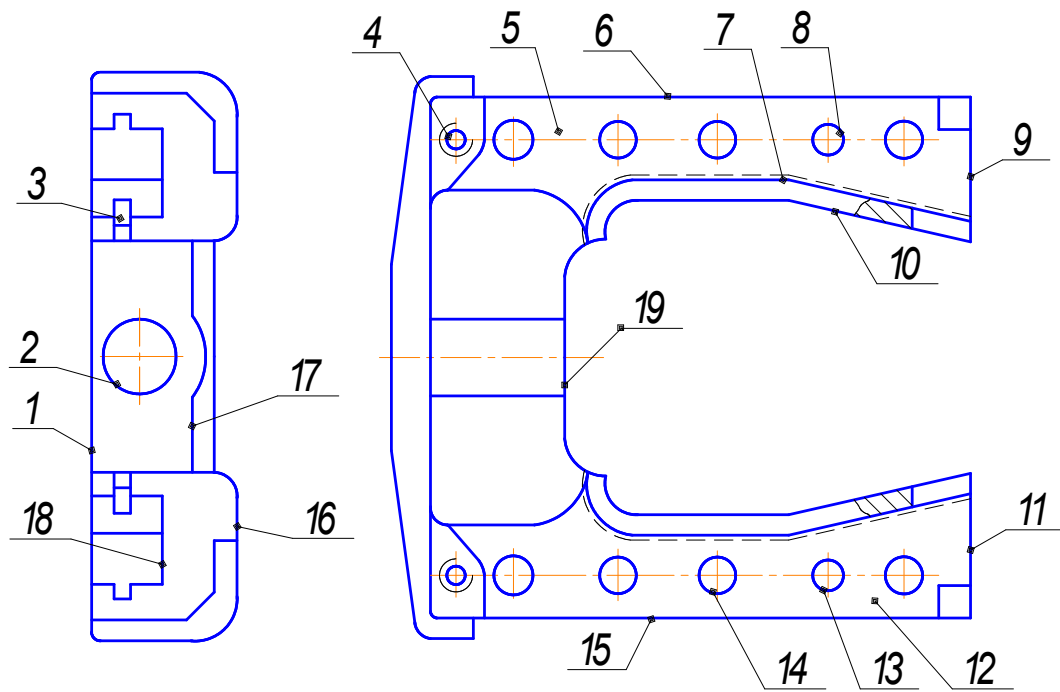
Ескіз деталі із вказанням основних поверхнь
